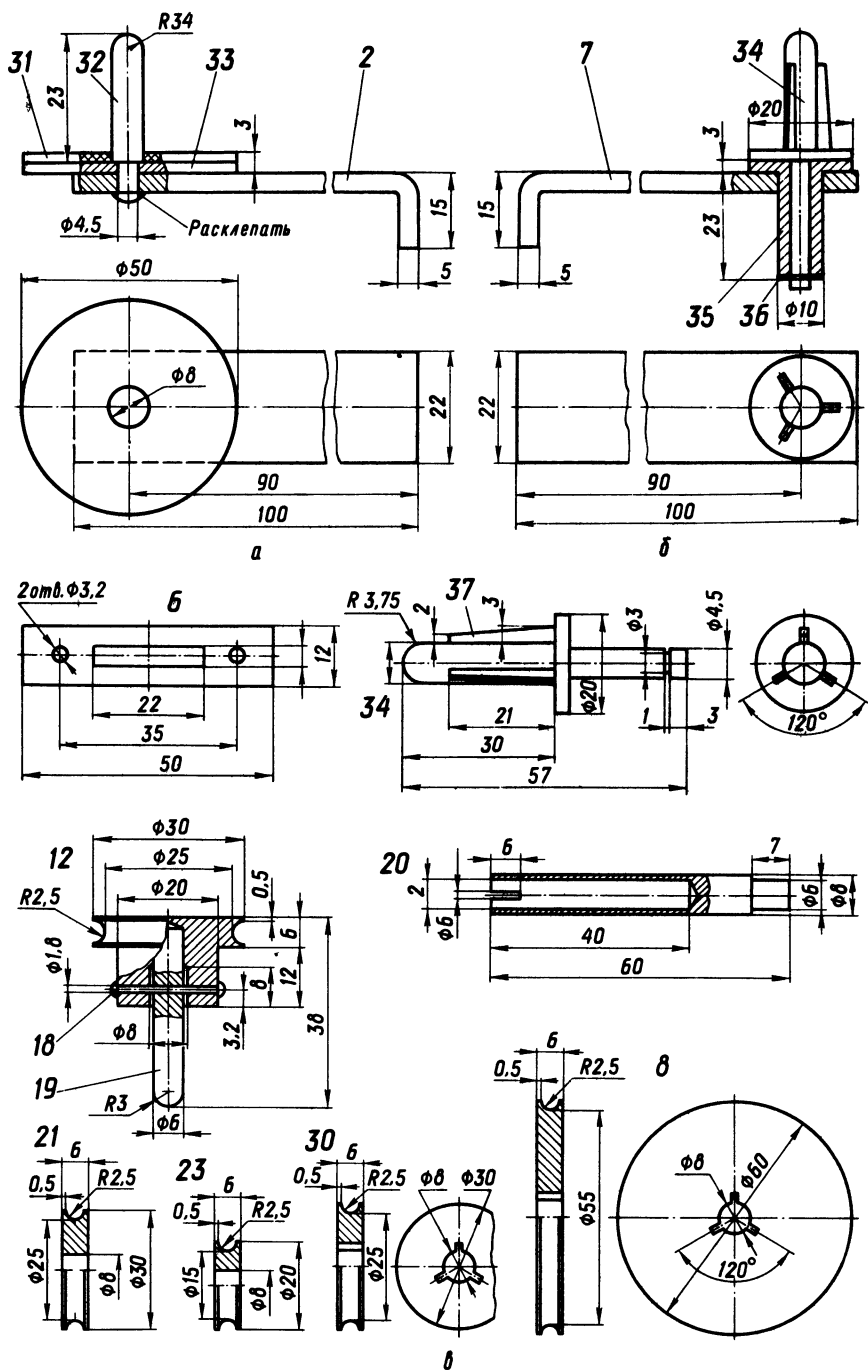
Подающий и приемный узлы, их детализовка и другие детали механизма привода.
